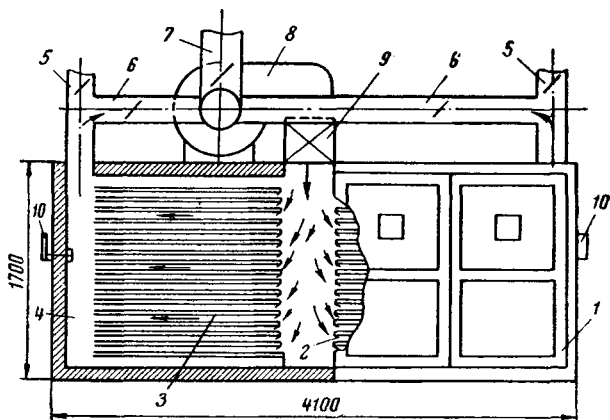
Сушилка шкафная для казенна с паровым калорифером:
